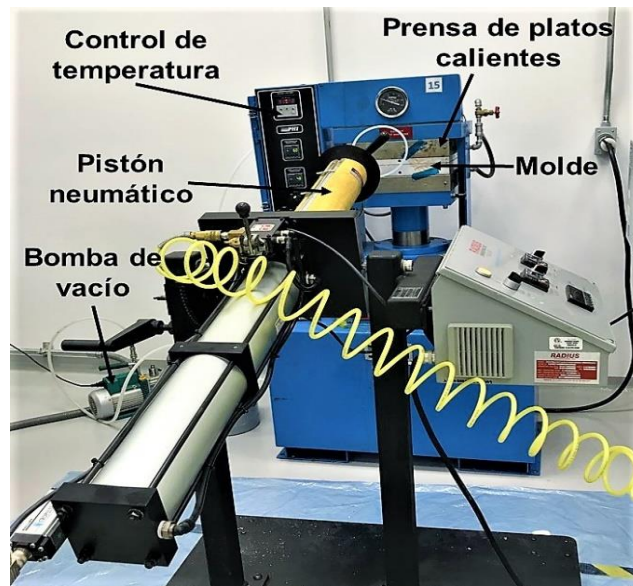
Equipo para el Moldeo por transferencia de resina (RTM).
